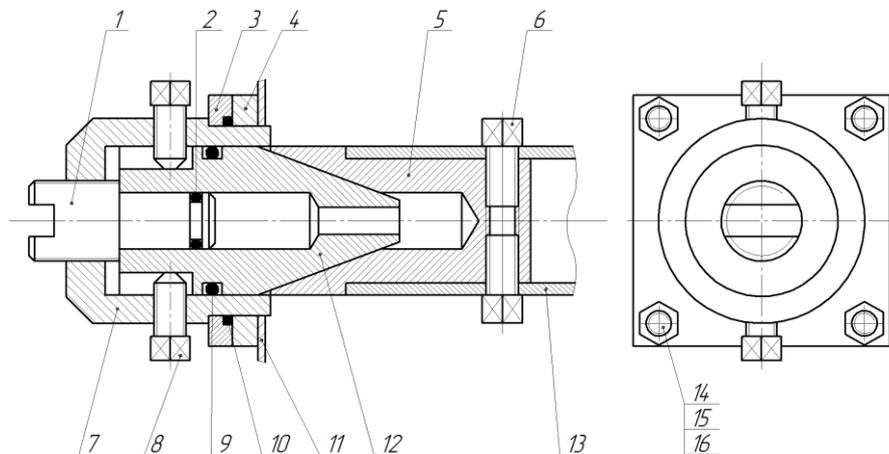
Конічний підшипник ковзання, що регулюється: 1 –гвинт притискний; 2 – кільце ущільнюоче; 3, 4 – фланець; 5 – вставка; 6 – гвинт; 7 – корпус; 8 – гвинт; 9, 10 – ущільнення гумове; 11 – корпус; 12 – цапфа; 13 – вал; 14 – шпилька; 15 – гайка; 16 – шайба
